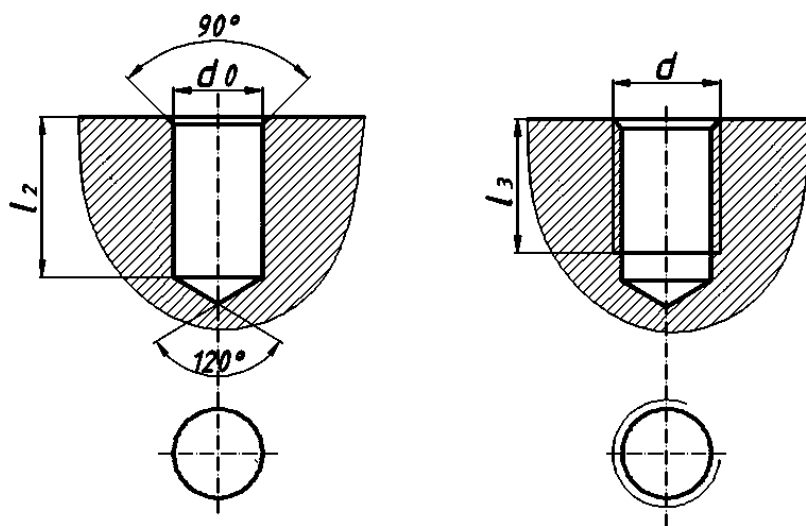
Образец оформления глухих резьбовых отверстий под шпильку
